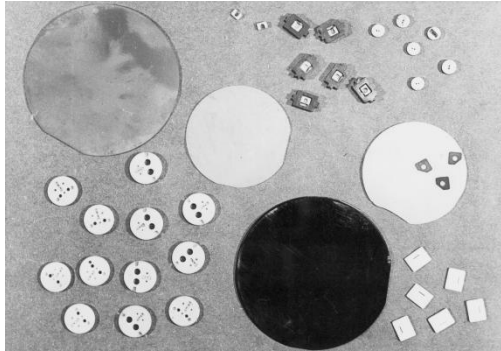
Детали, обрабатываемые на вибродоводочных станках
